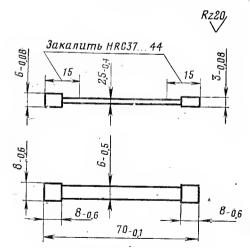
Шаблон для проверки спуска курка с боевого взвода
